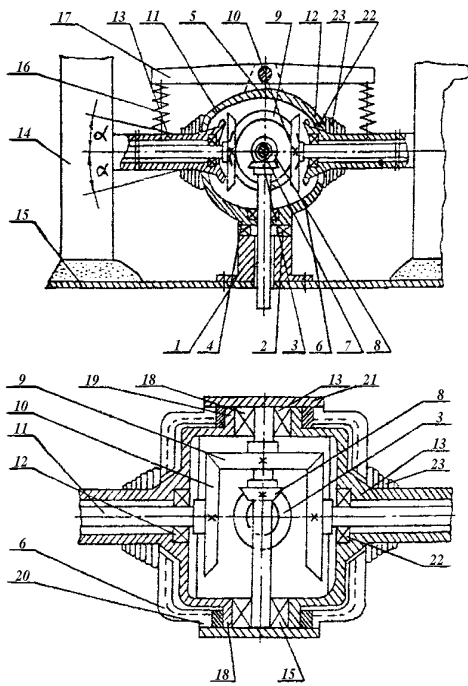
Схема привода катков смесителя: 1 – тумба; 2 – вал; 3 – шестерня; 4 – траверса; 5 – верхняя половина траверсы; 6 – нижняя половина траверсы; 7 – вал; 8,9 – шестерни; 11 – вал; 12 – подшипник; 13 – полые рычаги; 14 – катки; 15 – днище; 16 – пружины; 17 – коромысло; 18 – цапфы; 19 – кольца; 20 – отверстия; 21 – крышки; 22 – вертикальные прорези; 23 – гофр
